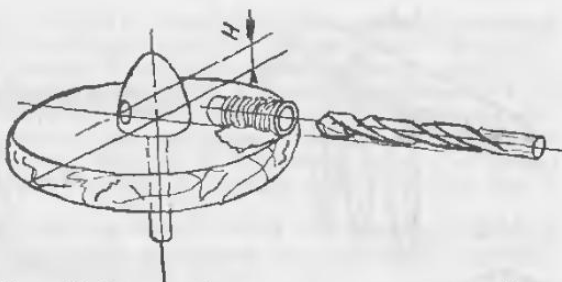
Приспособление для разметки отверстий под лопасти в коках винтов
